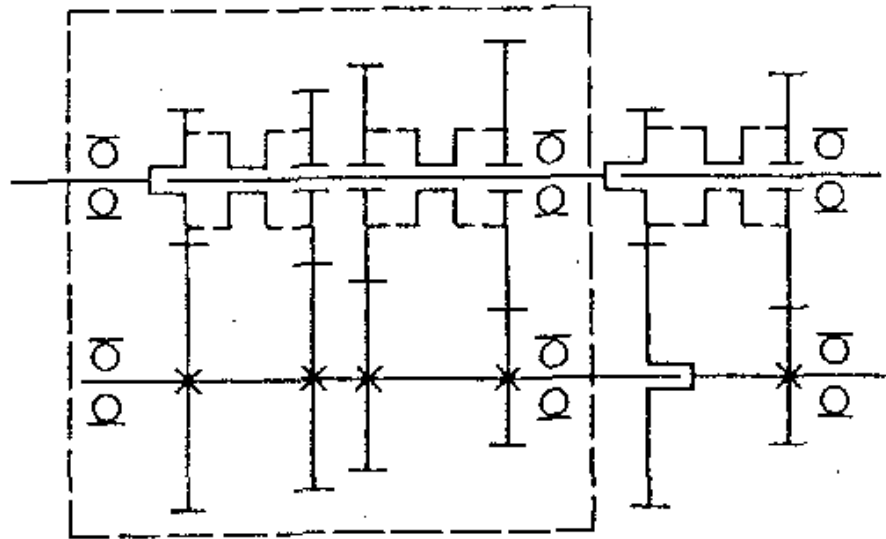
Схема «четырёхступенчатая коробка + двухступенчатый задний диапазонный редуктор»
